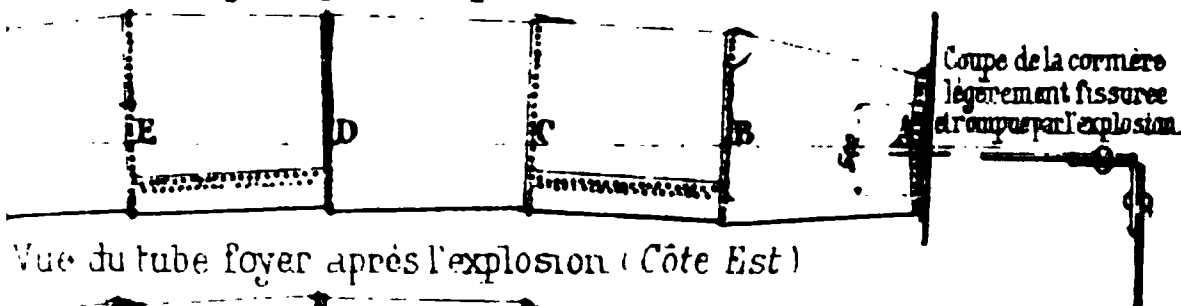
Vue du tube foyer après l'explosion (Côté Est)
